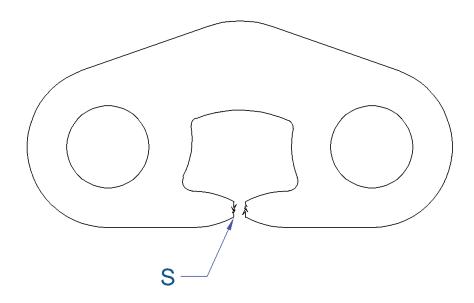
Section « S » de la plaque d'essai ATP (section de rupture).
